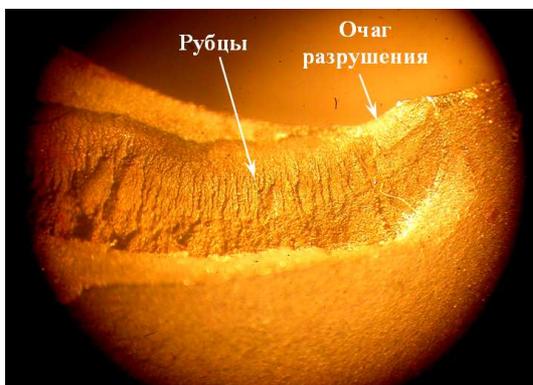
Очаг разрушения и рубцы на поверхности излома камеры сжатия
